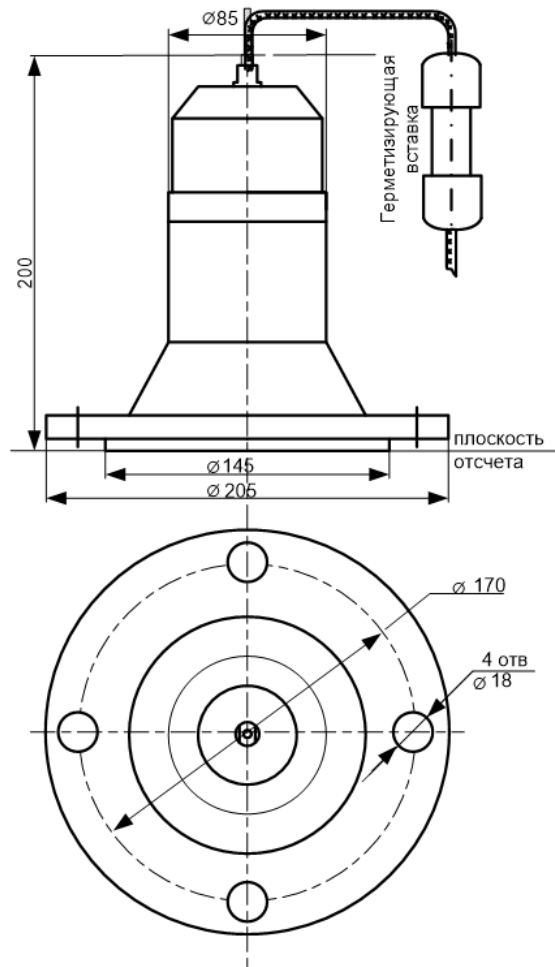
Габаритные и установочные размеры акустического преобразователя АП-11
